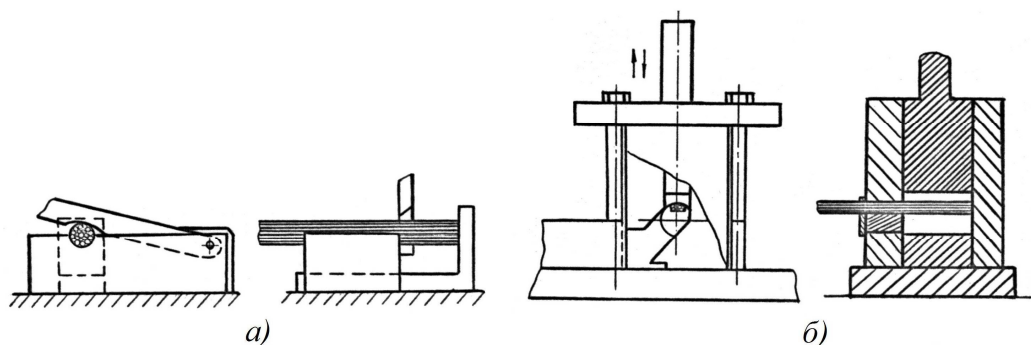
Способы резки проволоки в пучках: а) резка ножницами; в) рубка в штампе
